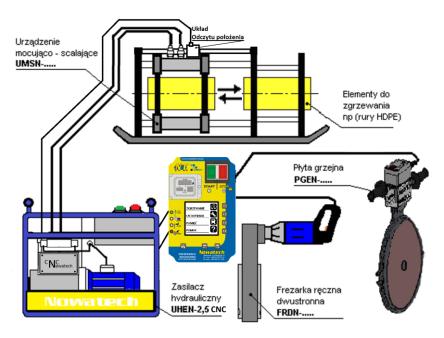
Блок-схема аппарата для стыковой сварки типа ZHCN-CNC
